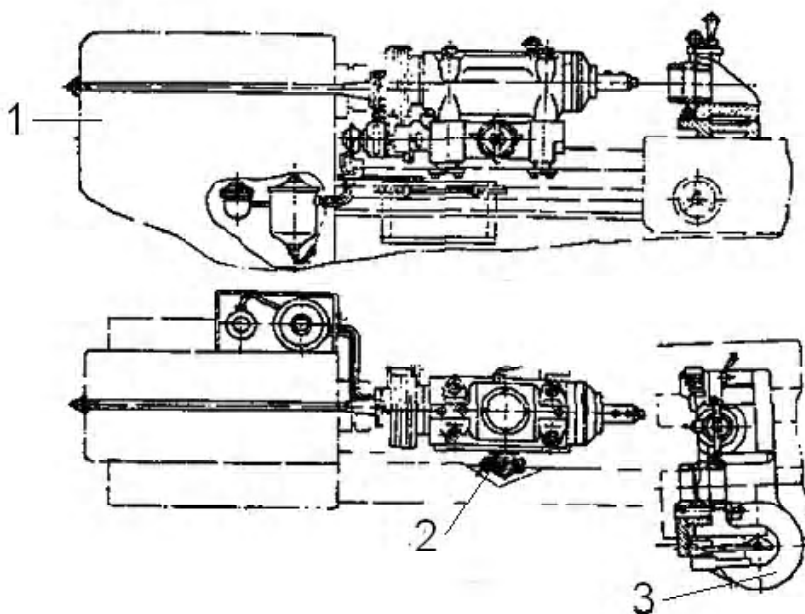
Приспособление для растачивания втулки верхней головки шатуна: 1 – токарный станок 1616, 2 – расточная головка, 3 – устройство для укладки шатуна.
